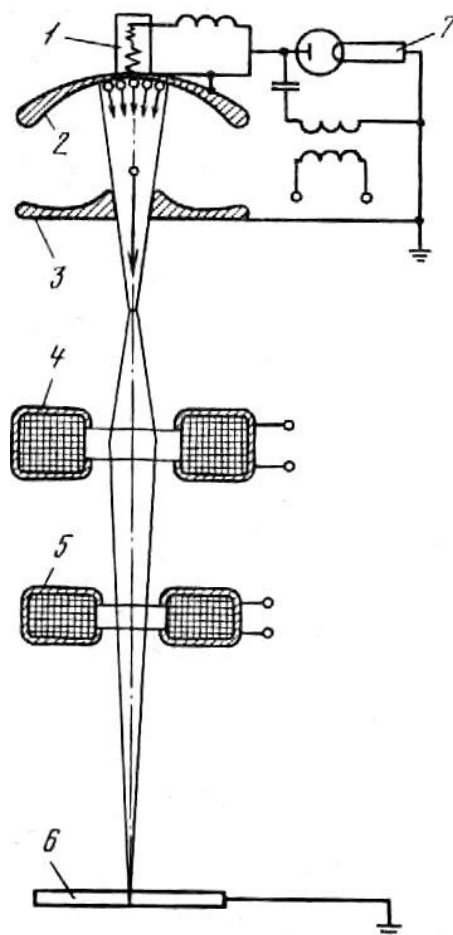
Схема установки для сварки электронным лучом
